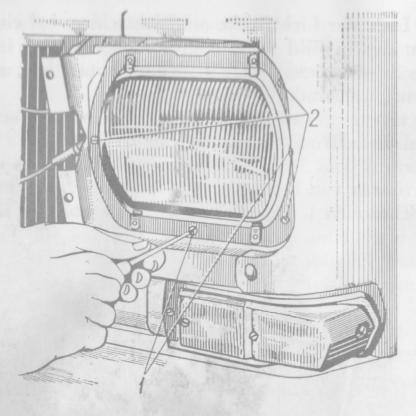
Scheinwerfer des Kraftwagens: 1 – Stellschrauben des Optikelementes; 2 – Befestigungsschrauben
